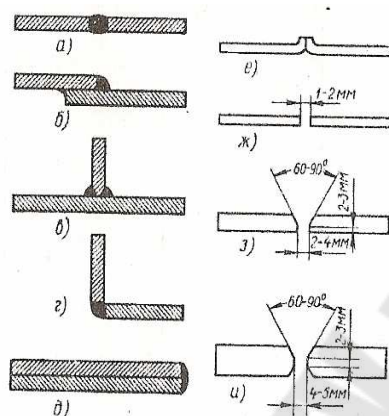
Типы сварных соединений и подготовка кромок сварного шва: а - стыковое; б - внахлестку; в - тавровое; г - угловое, д - боковое, е, ж, з, и - подготовка кромок
